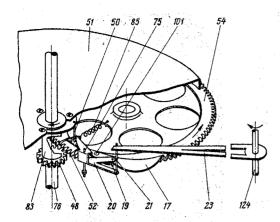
Кинематическая схема включения механизма смены пластинок; 17 — пластина; 19 — палец; 20 — рычаг; 21 — штифт; 23 — рычаг звукоснимателя; 48 штирт, 29 — рычаг звукоснимателя, 48 — шестерня; 50 — штирт; 51 — маховик; 52 сектор зубчатый; 54 — шестерня; 75 — ось; 76 — вал; 83 — полый вал; 85 — пружина; 101 — ось, винт $M2,5 \times 8$; 124 — ось звукоснимателя.
